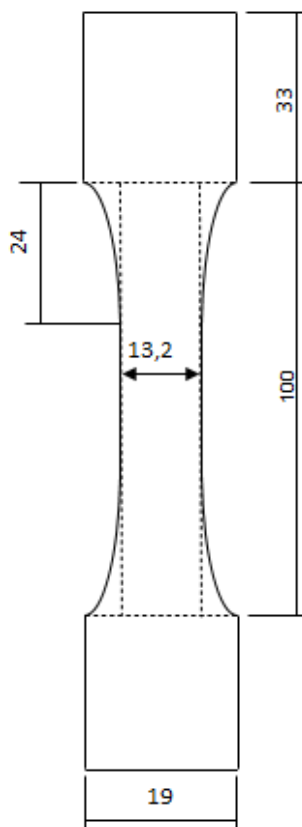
Dimensões corpo de prova (Do autor, 2020).
